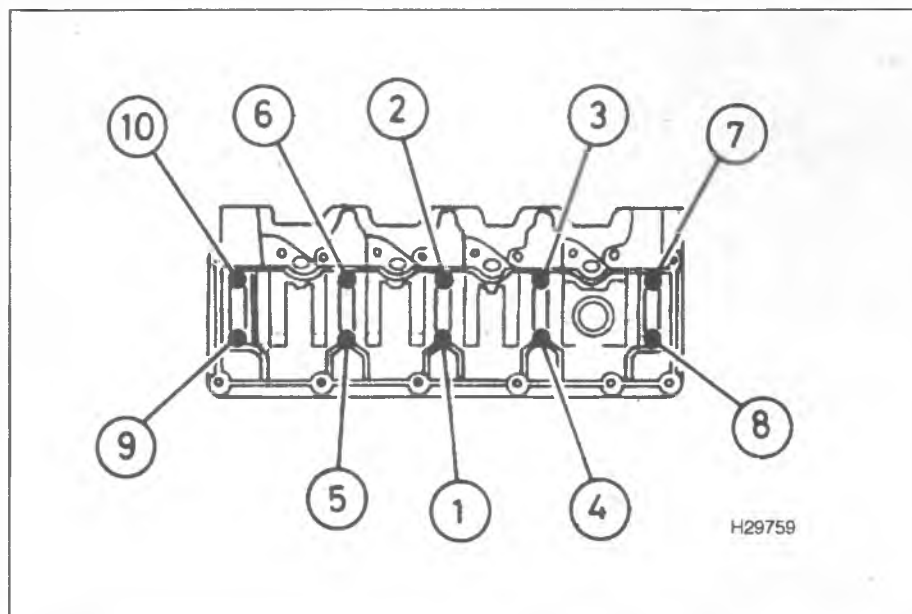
Последовательность затяжки болтов корпуса подшипников распределительного вала
